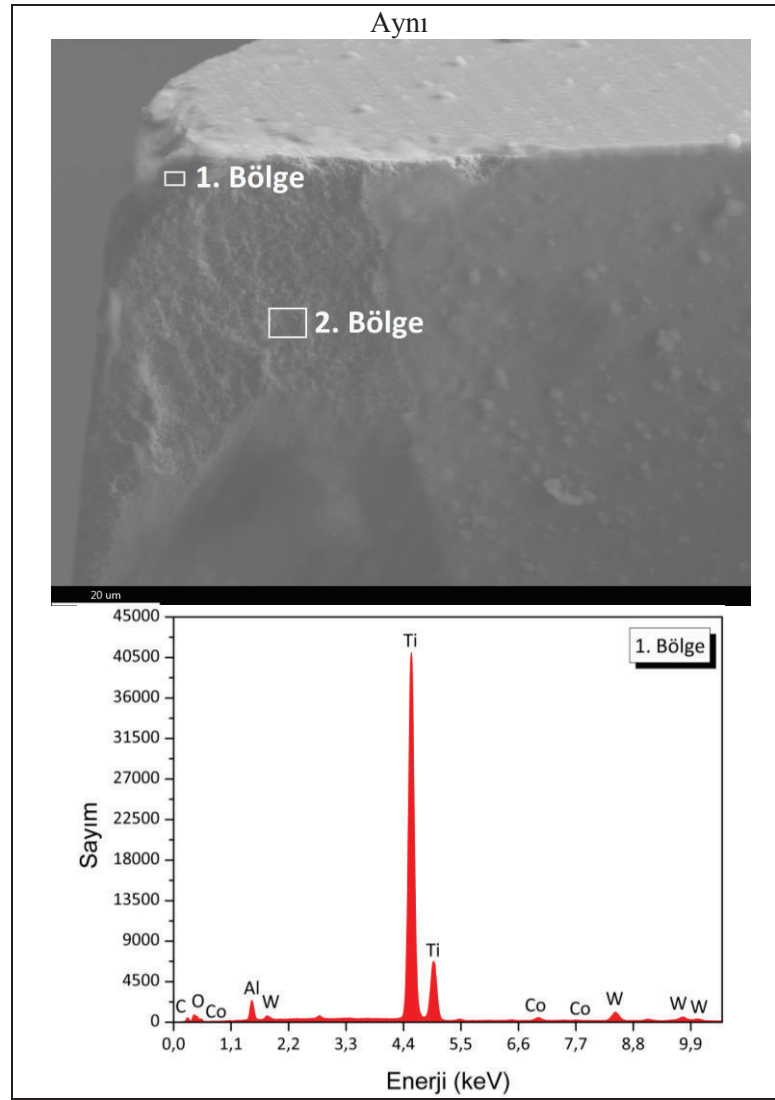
Ti6Al4V malzemesinin 75 mm/dak ilerleme hızında yüksek hız kafası ile 28000 dev/dak devir sayısında mikro yüzey frezelemede takım yollarının kesici takım ve iş parçası yüzeyi üzerindeki etkisi (f: İlerleme, a_e: Yana kayma mesafesi).
